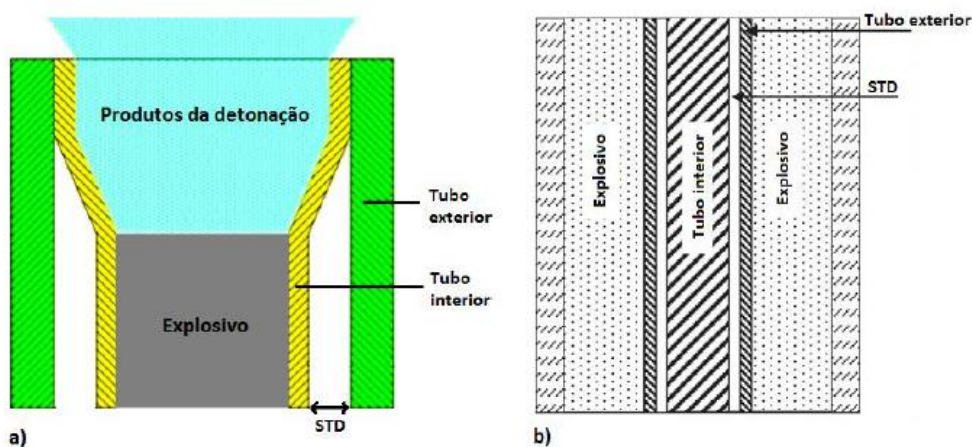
Representação esquemática de uma configuração cilíndrica: a) explosivo interior, adaptada de Sun *et al.* [11]; b) explosivo exterior, adaptada de Mendes *et al.* [12].
